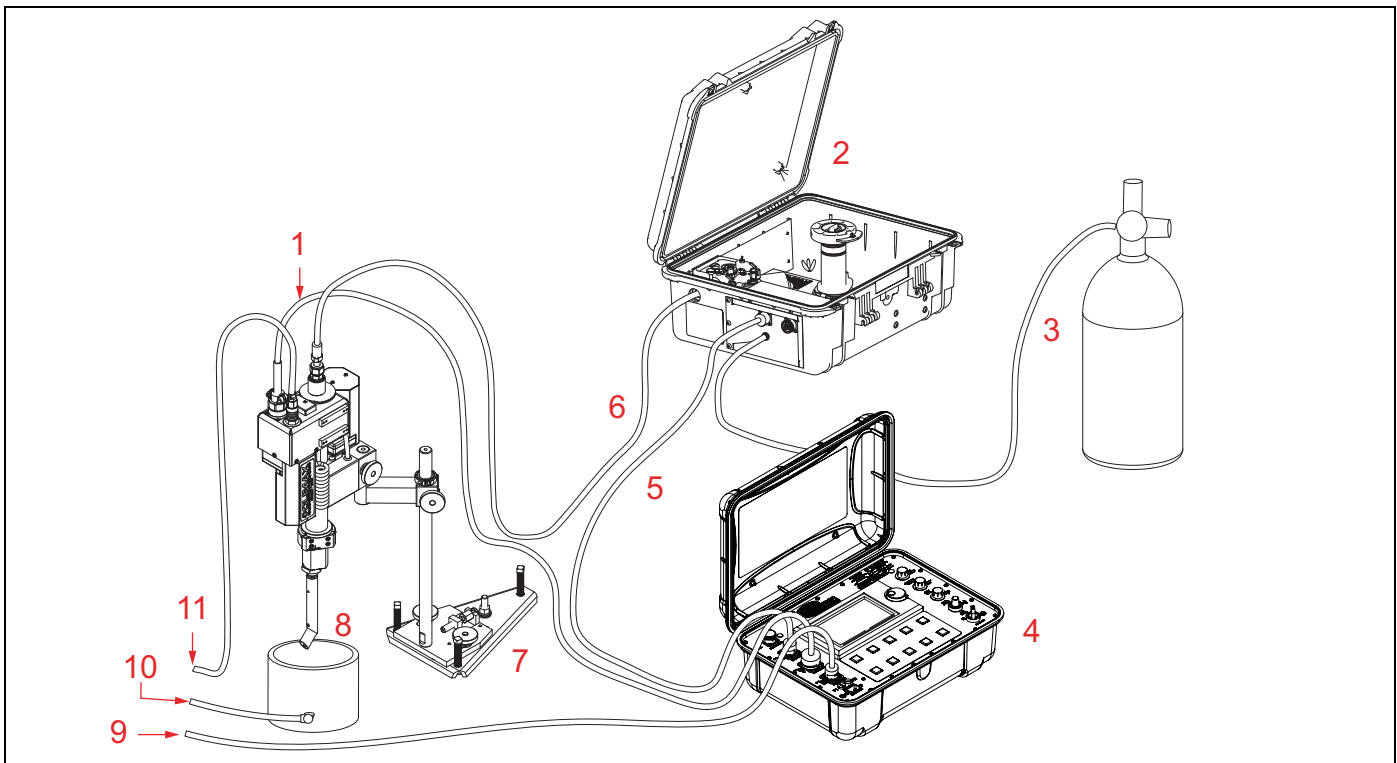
BW3000 AUTOBOREWELDER Y COMPONENTES EXTERNOS
